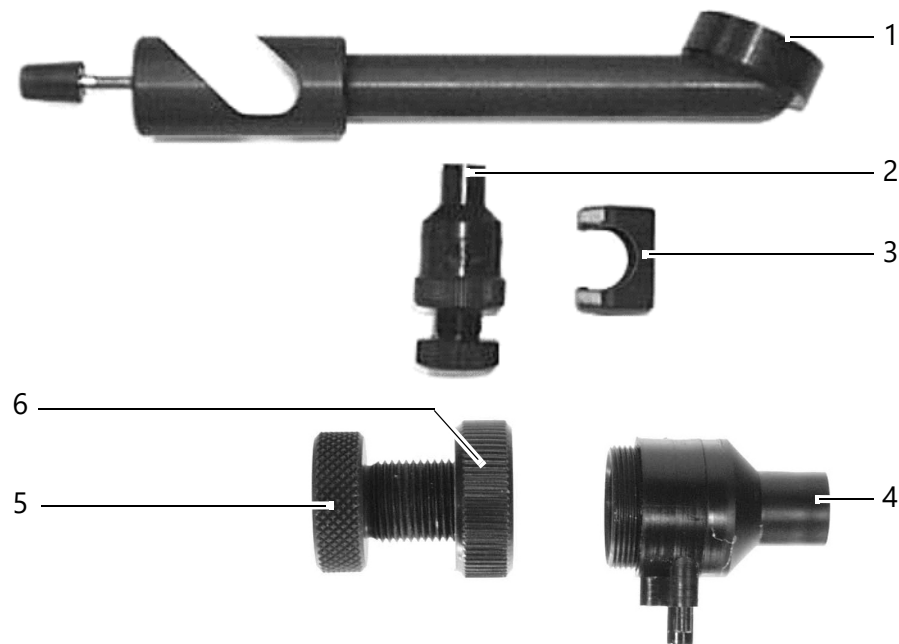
Pièces de montage pour la mesure des faces postérieures des lentilles de contact
